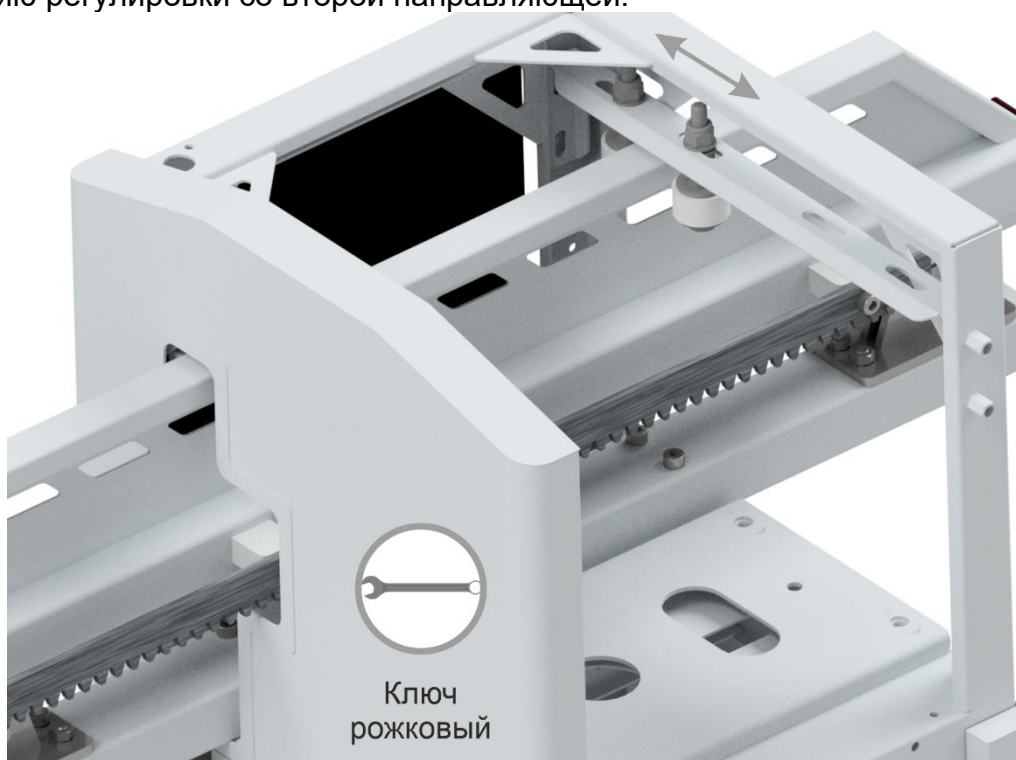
Регулировка верхних роликовых направляющих.
